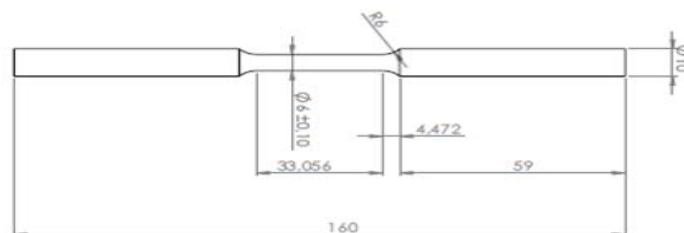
Desenho do Corpo de prova para ensaio de tração a quente.
